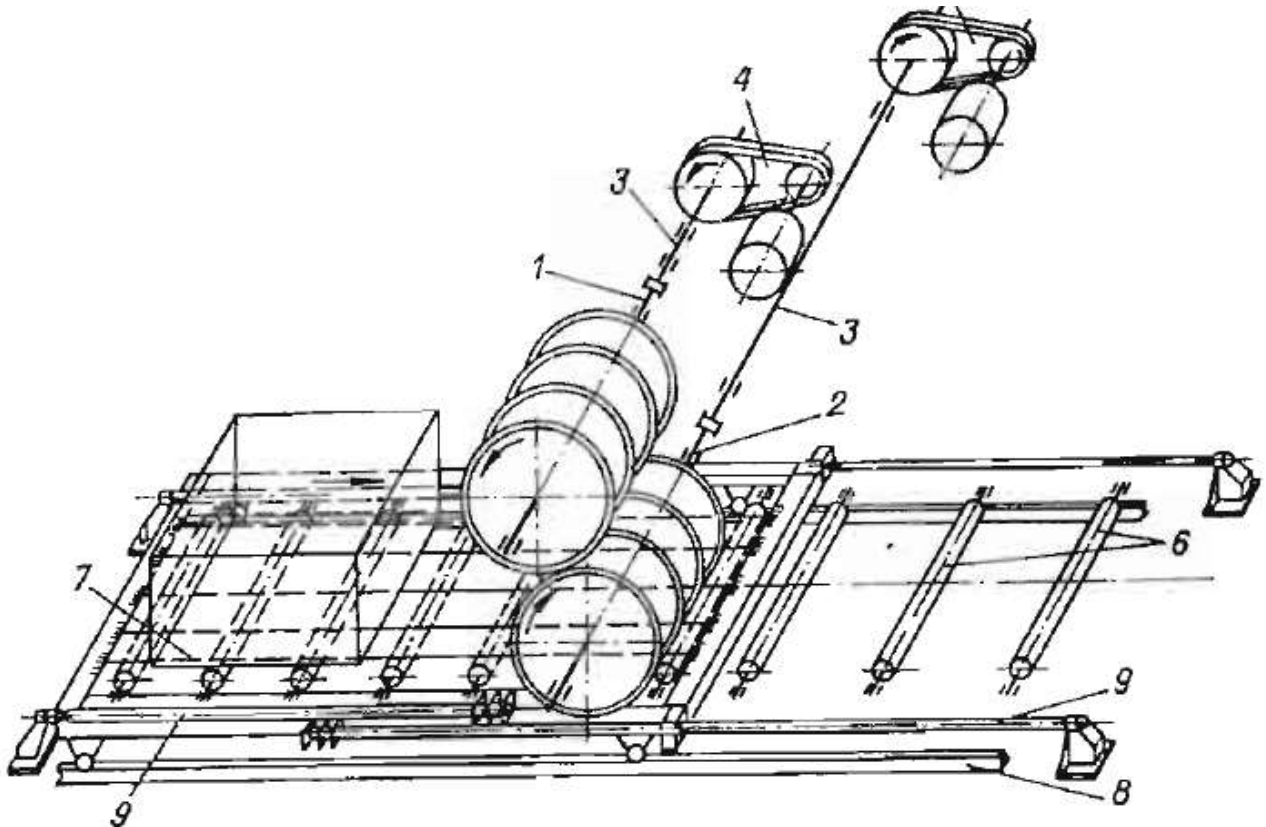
Кінематична схема розпилювального багатодискового двовального верстату мод.СМР-017. Позначено: 1 – верхній пильний вал; 2 – нижній пильний вал; 3 – проміжний вал; 4 – привод верхнього валу; 5 – привод нижнього валу; 6 – рольганг; 7 – візок; 8 – рейковий шлях; 9 – гідроциліндри поздовжньої подачі візка [23].
